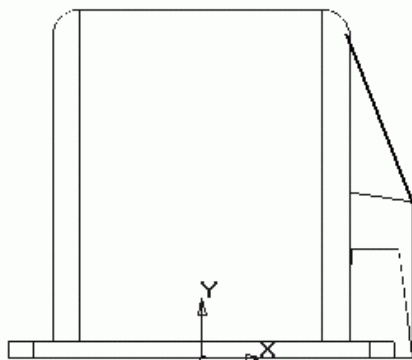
Эскиз ребра жесткости крышки редуктора
